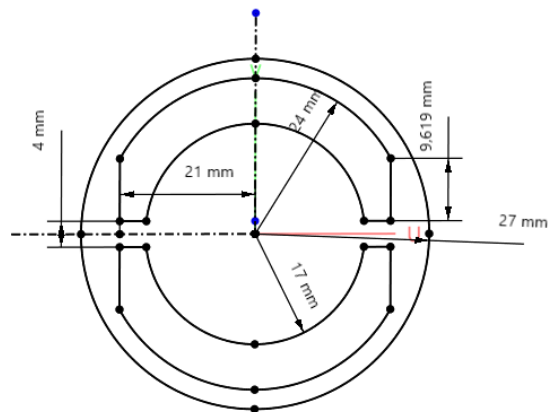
Dimensiones geométricas del diseño de la base de la pieza 9.
